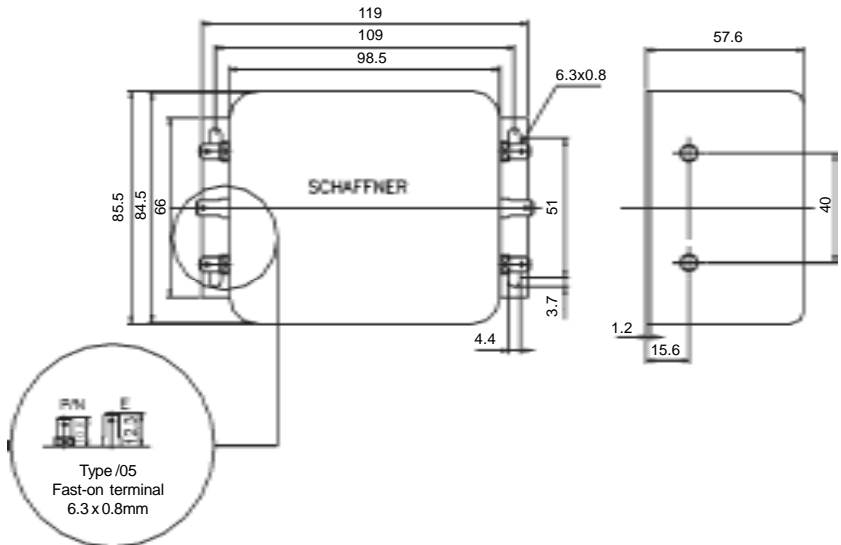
Чертеж внешнего фильтра FS6007-16-06
